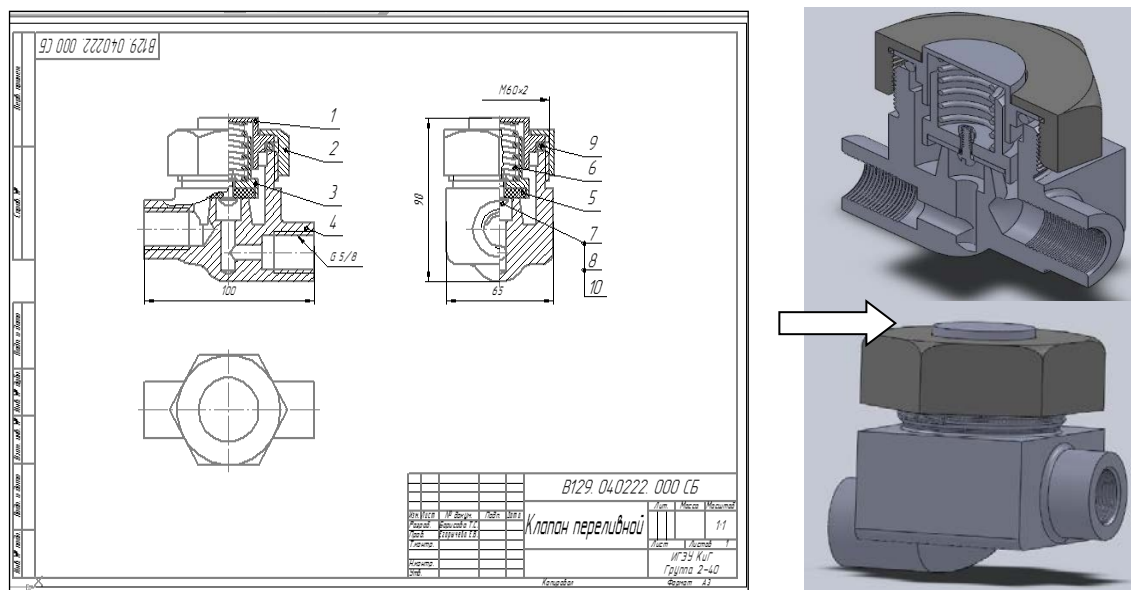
Сборочный чертеж и трехмерная модель сборки «Клапан переливной»
